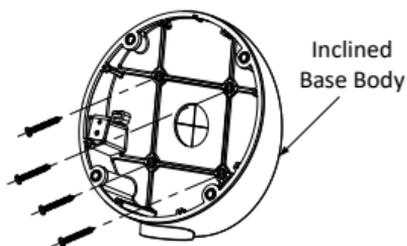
Fixez le boîtier du support inclinable au plafond/mur
